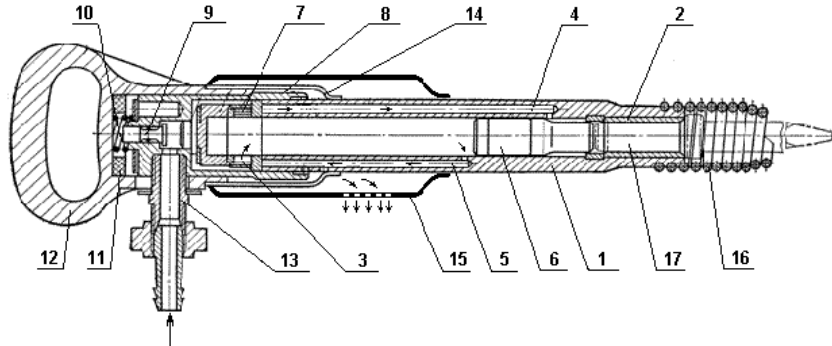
Конструкция современного пневматического отбойного молотка
